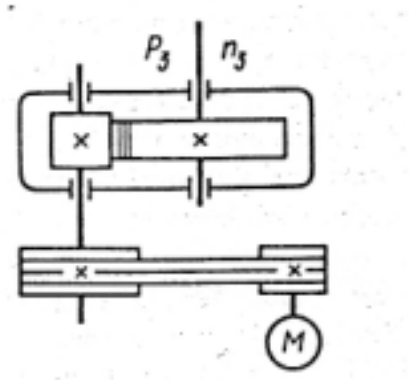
Исходная схема цилиндрической прямозубой передачи
